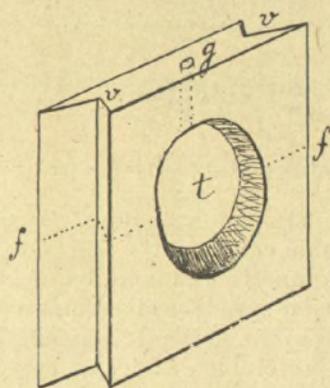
Confection d'un coussinet en deux pièces pour lunette fixe à cage carrée.
